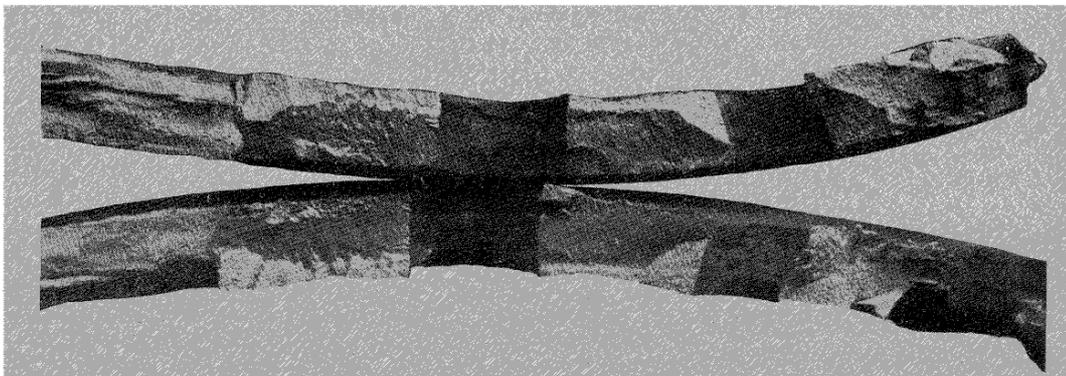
Vue des deux faces d'une cassure de tôle à la suite d'une fissuration produite au poinçonnage.
